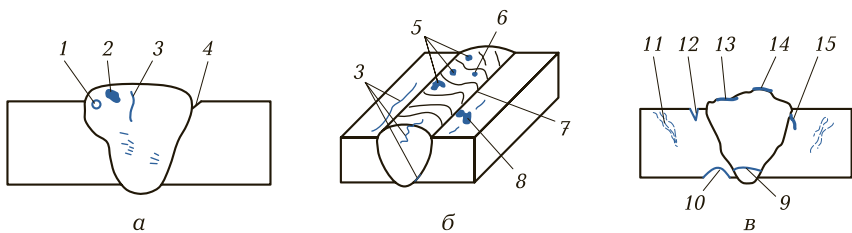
Основные дефекты в сварных соединениях:
